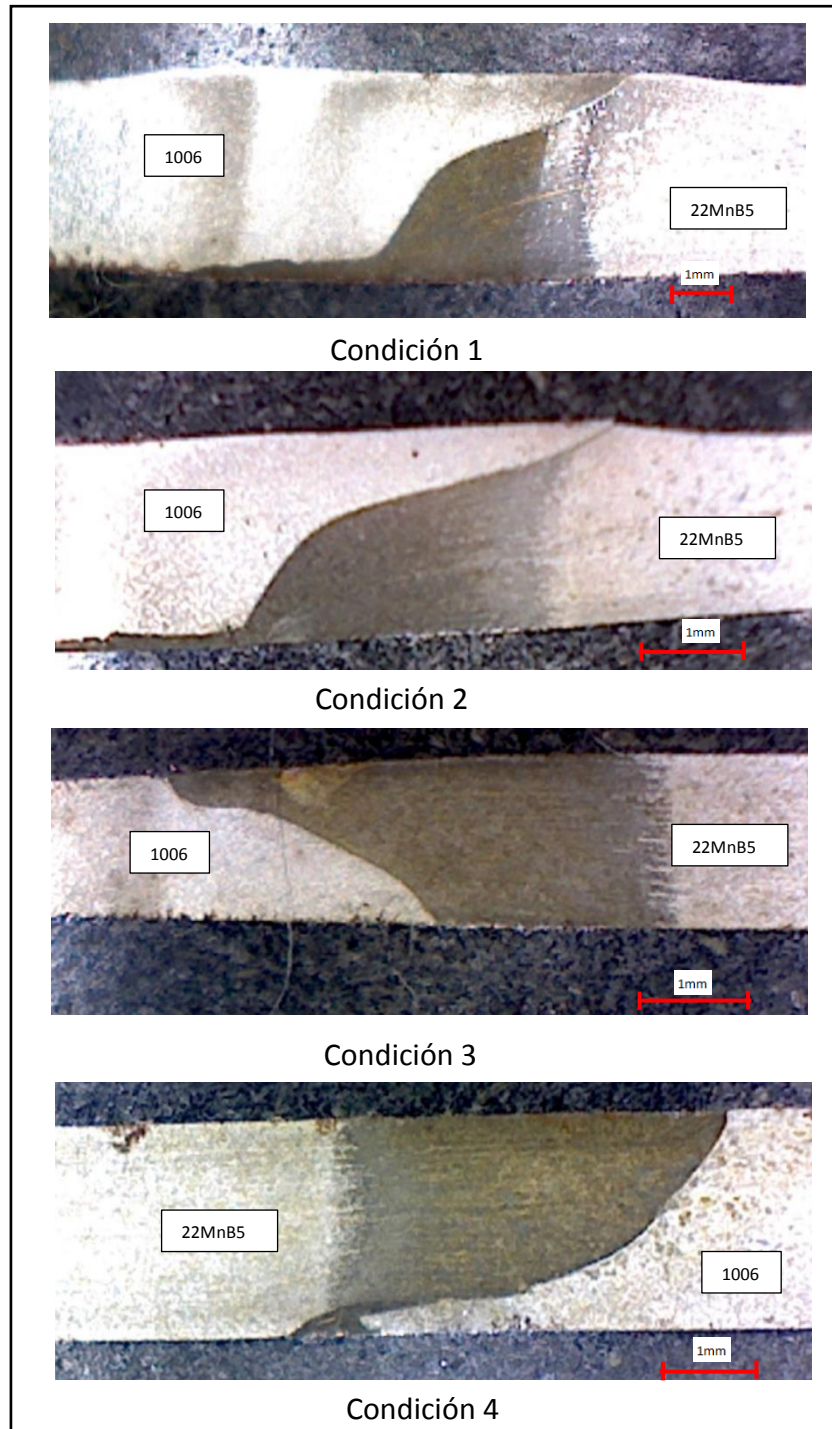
21. Sección transversal del cordón de soldadura para cada condición de la unión 22MnB5-1006.
